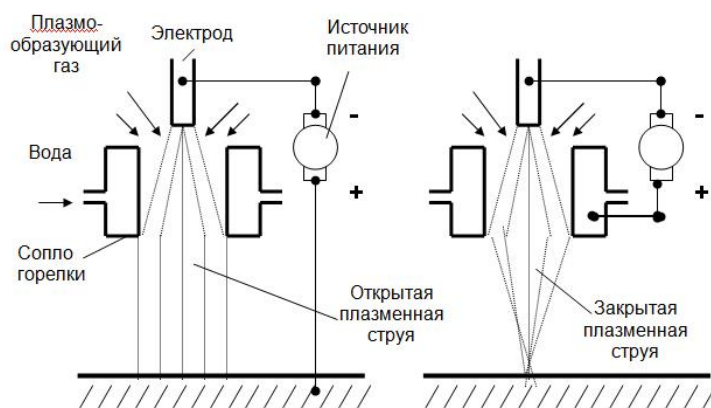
Схема плазменной сварки открытой и закрытой плазменной струей
